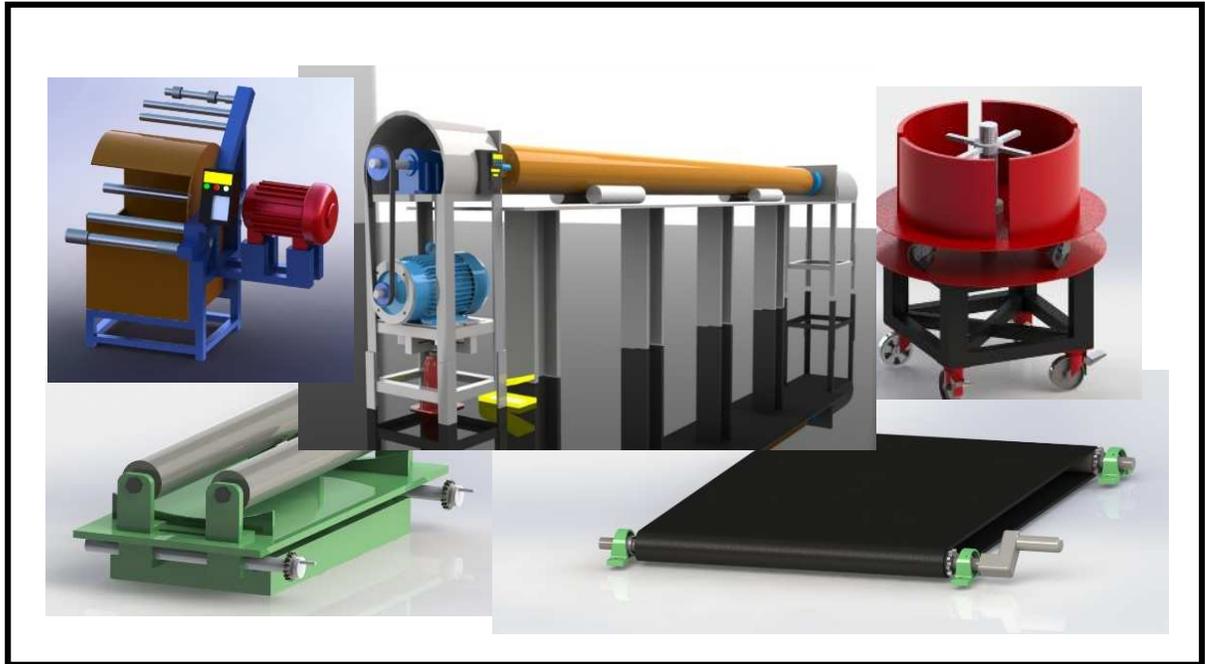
En la actualidad Ingeniería se encuentra desarrollando dispositivos y maquinas que tendrán funcionamiento en la planta nueva que se encargara de realizar mangueras de hasta 60 m. de longitud
